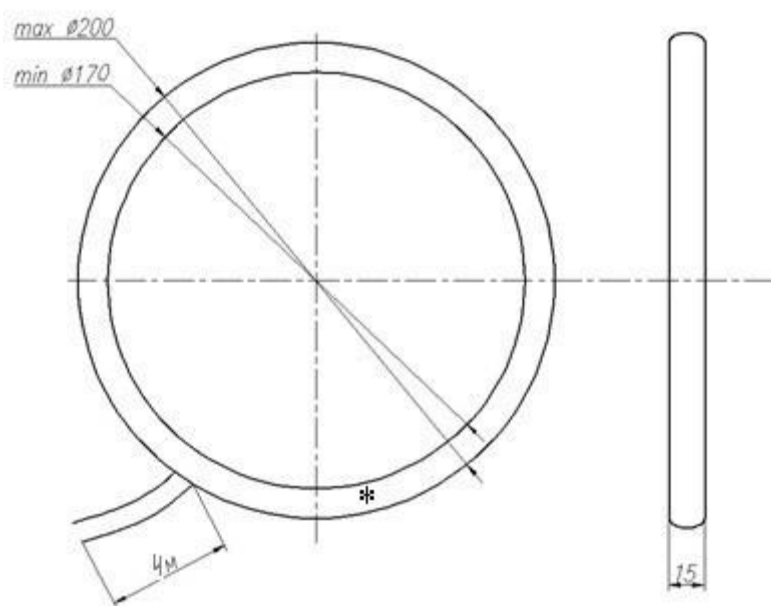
Габаритный чертеж трансформатора тока ТТ170
